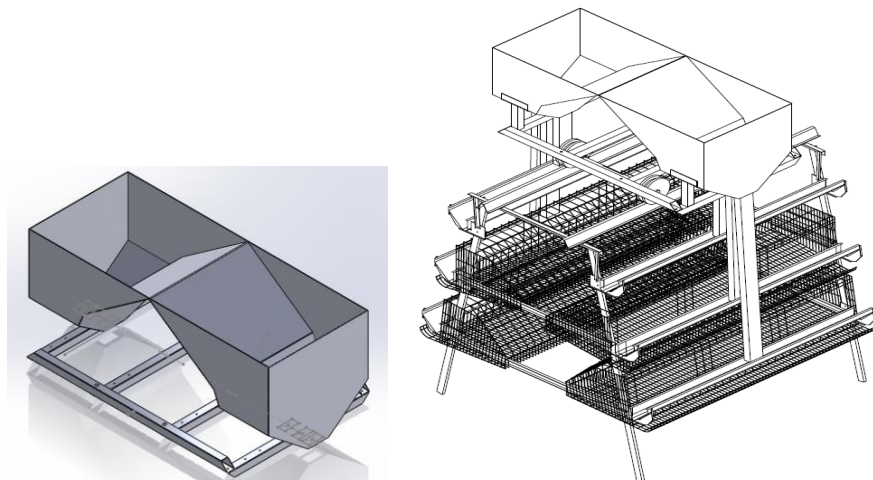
Diseño del ensamble de tolva y ensamble final
